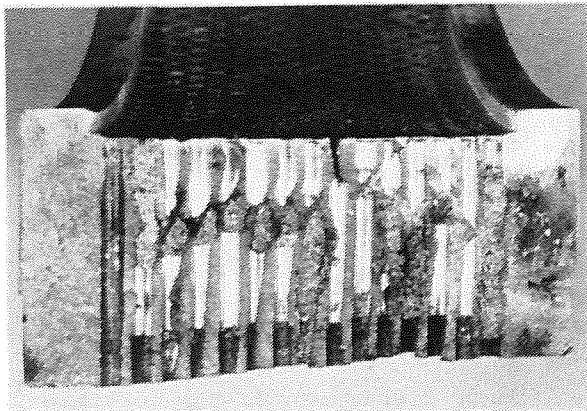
Aspecto superficial de la fractura de la matriz. En la parte superior derecha pueden apreciarse las señales de la grieta que ha causado la rotura (x 0,5).
